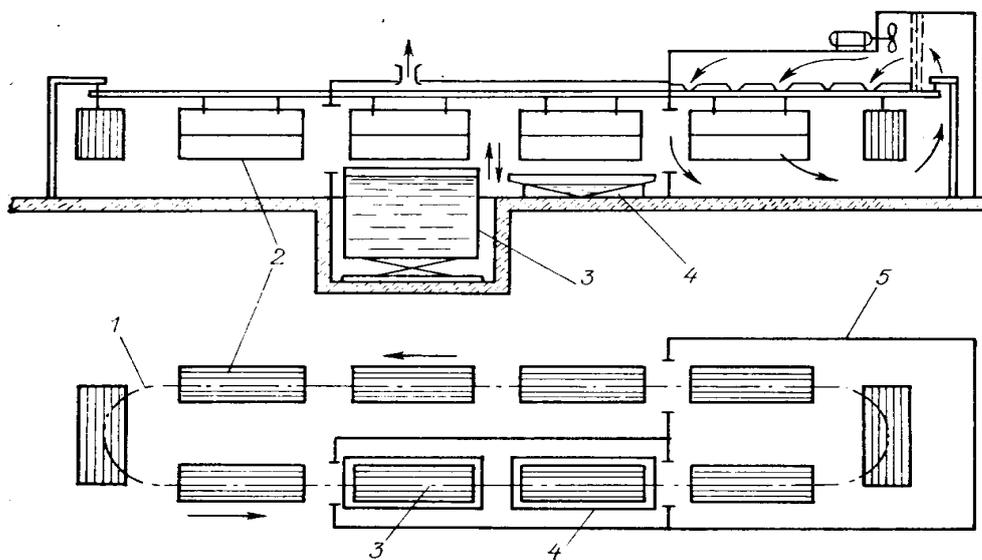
Схема линии пропитки окунанием: 1 – подвесной круговой
